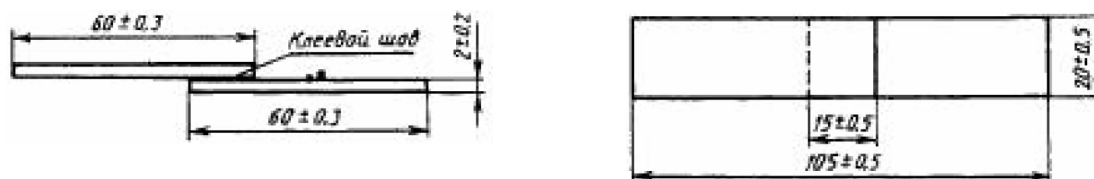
Форма и размеры (в мм) образца согласно ГОСТу 14759–69
